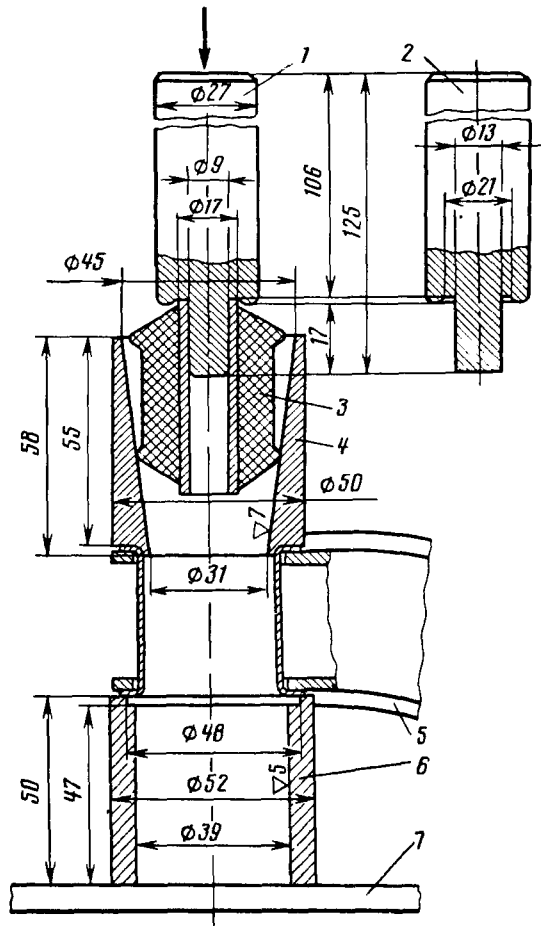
Запрессовка сайлент-блока в гнездо рычага передней подвески:
